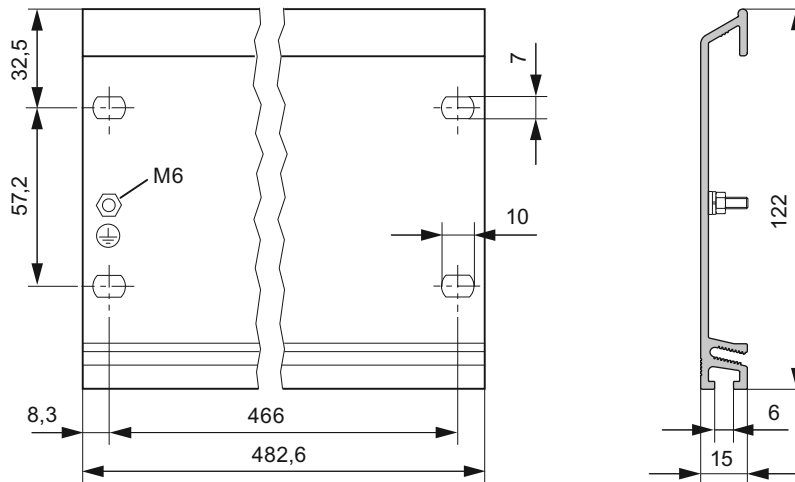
Croquis acotado del perfil soporte en ancho estándar de 482,6 mm
